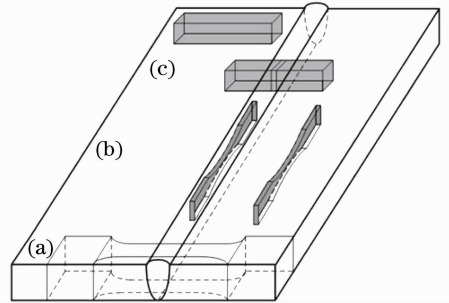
拉伸、冲击试样取样位置示意图。(a)焊接接头拉伸试样;(b)焊缝金属、母材拉伸试样;(c)焊缝金属、母材冲击试样
